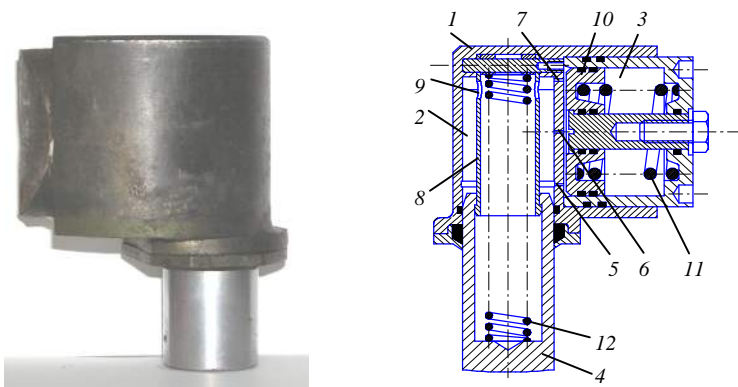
Внешний вид и конструкция опытного гидробуфера:
